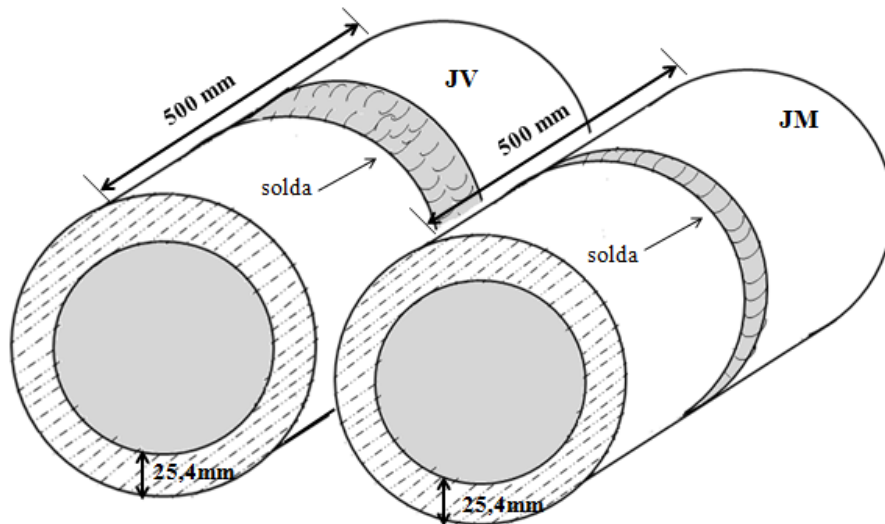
Representação do material como soldado (CS): junta (JV) e (JM).
